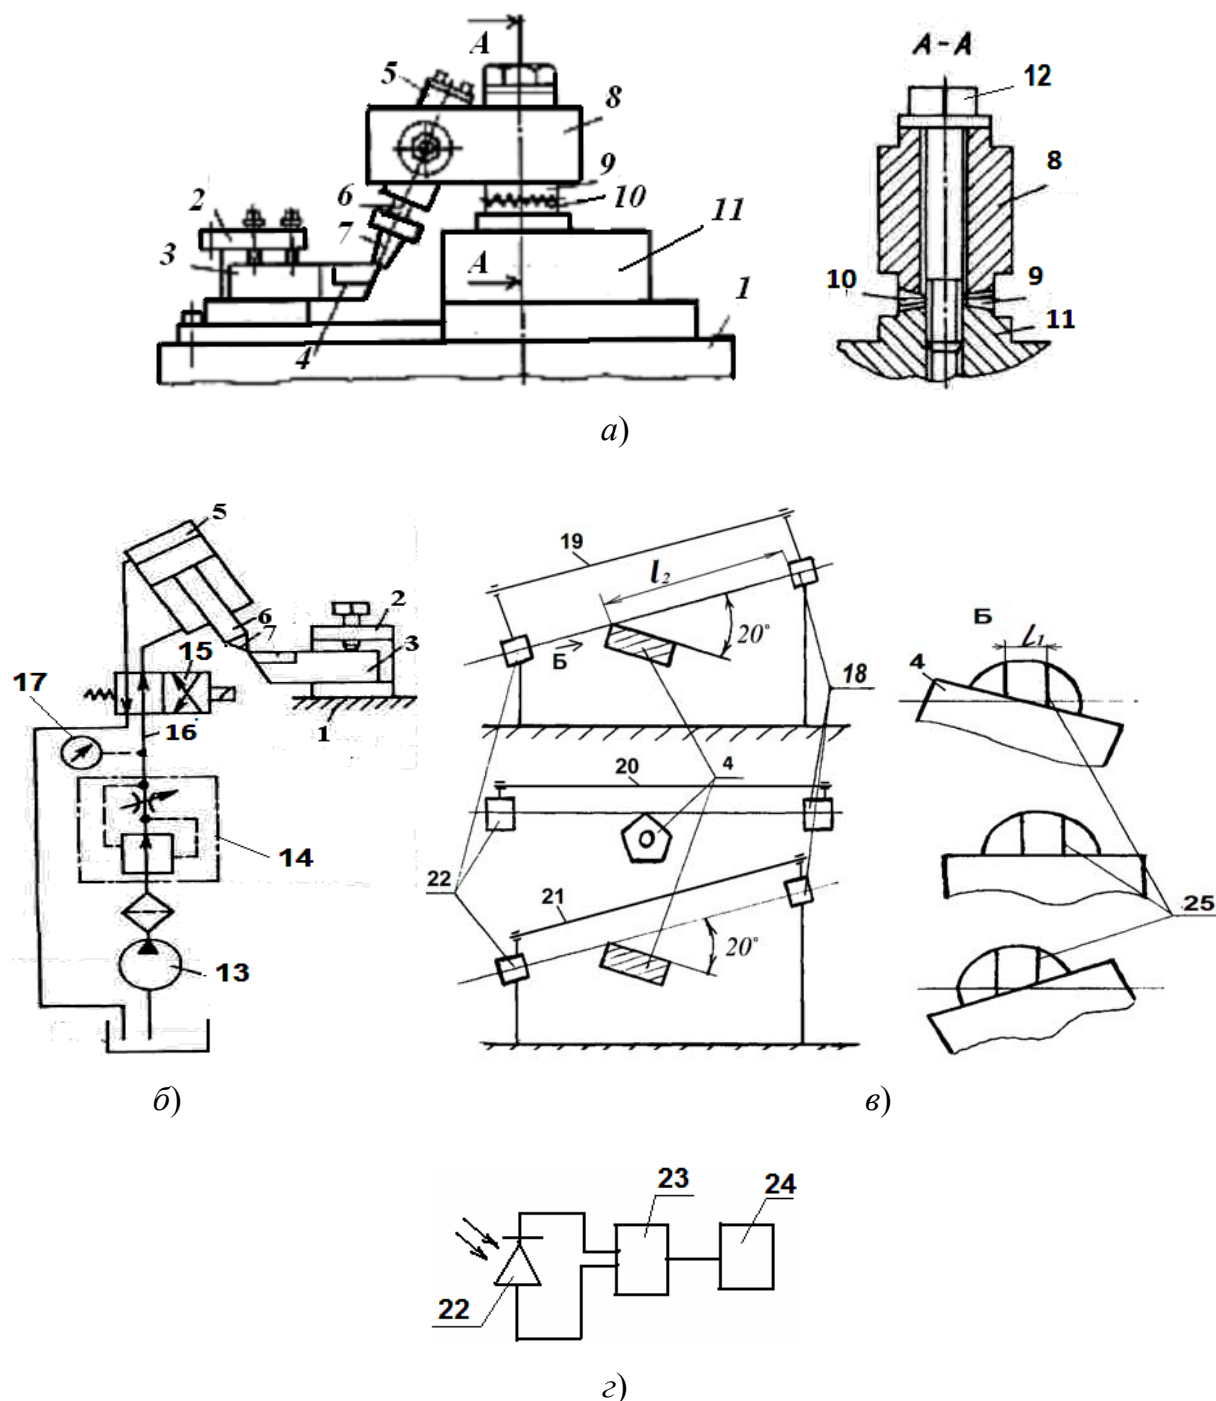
Эскиз стенда для испытания резцов на статическую точность: а – нагружающее устройство; б – принципиальная схема; в – схема измерительного устройства; г – считывающее устройство
